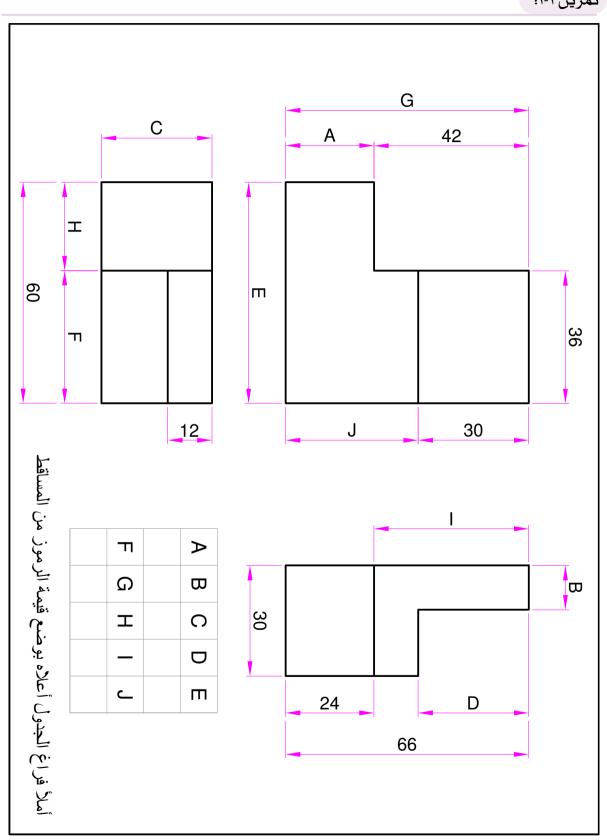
٧- ب: استنتاج المسقط الجانبي من مسقطين
